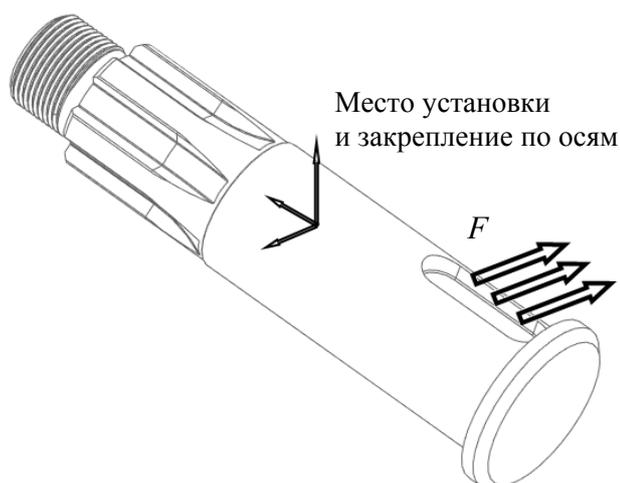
Схема нагружения и закрепления приводного вала
